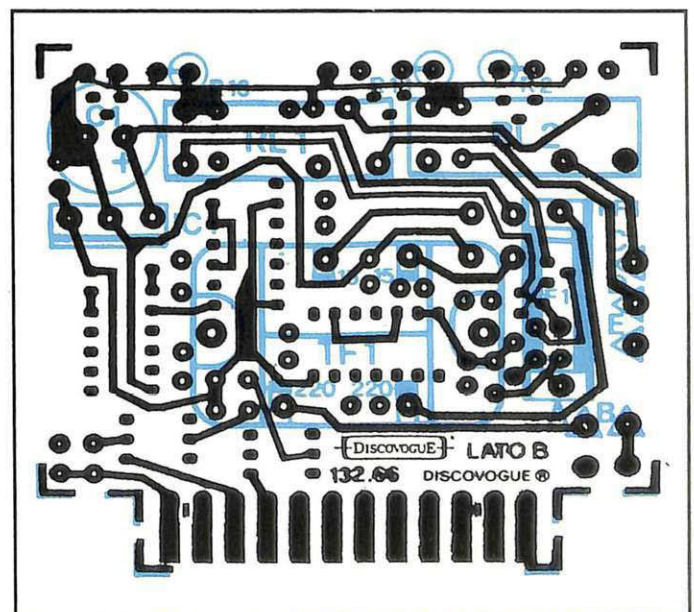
Pista conduttrice del lato B del circuito stampato principale con componenti montati.
